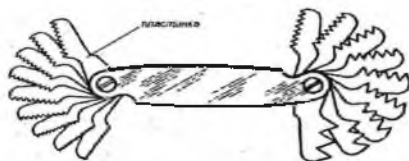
Резьбовой шаблон [10, с. 297]
